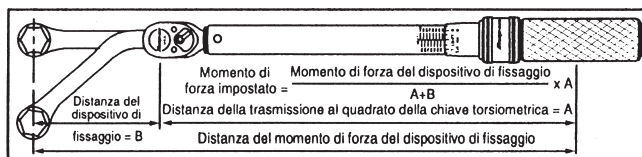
Il momento di forza del dispositivo di fissaggio è maggiore del momento di forza della trasmissione al quadrato della chiave torsionometrica.
